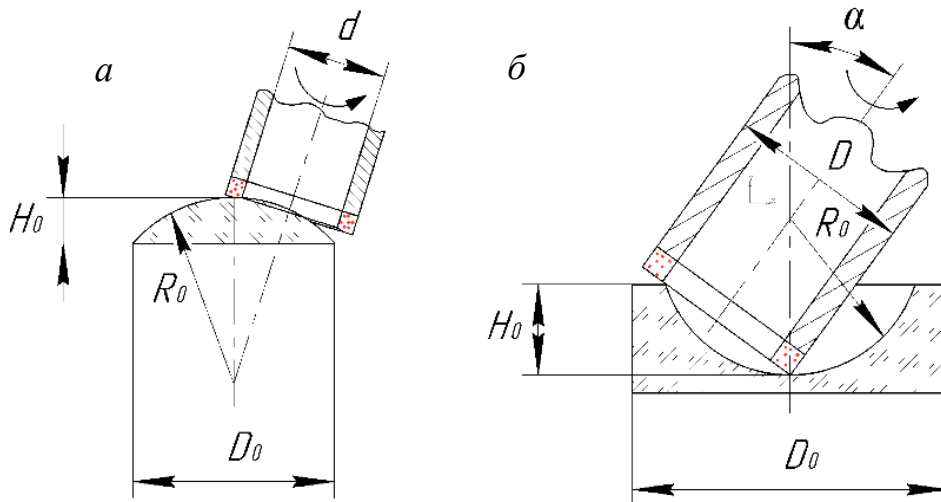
Выбор трубчатого инструмента для обработки сферической поверхности
